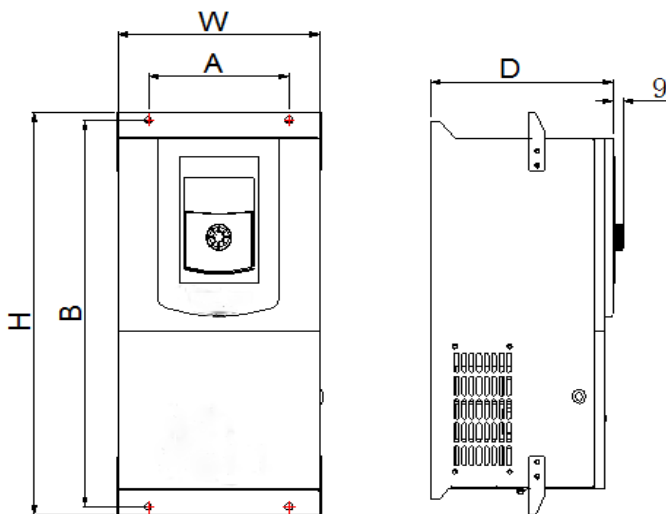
11~37KW 钣金机箱外形尺寸及安装尺寸示意图
